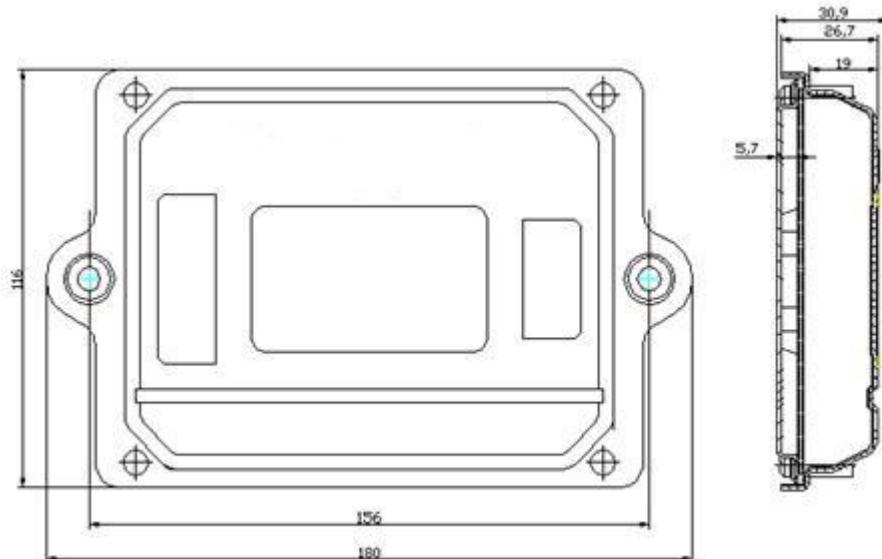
DX202,DX102 安装尺寸/Fig.6-1-2 Installing Dimension of DX202 and DX102
